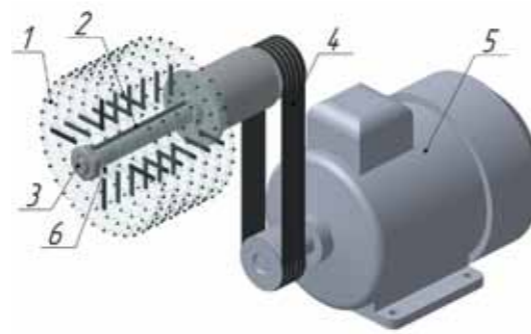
Привод вращения инструмента: 1 – пила; 2 – шпонка; 3 – пильный вал с опорами и шкивом; 4 – ремень; 5 – электродвигатель со шкивом; 6 – дистанционная втулка
